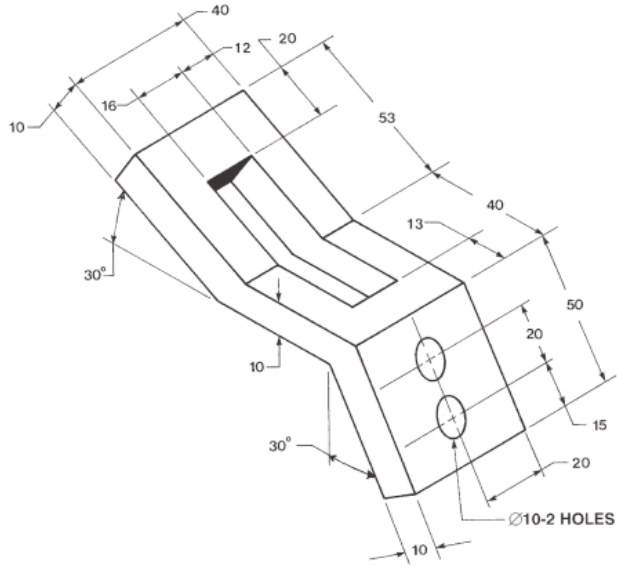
figura construida en MMGS se debe elegir por parte del diseñador el plano de trabajo que más información proporcione para la construcción de la pieza.
